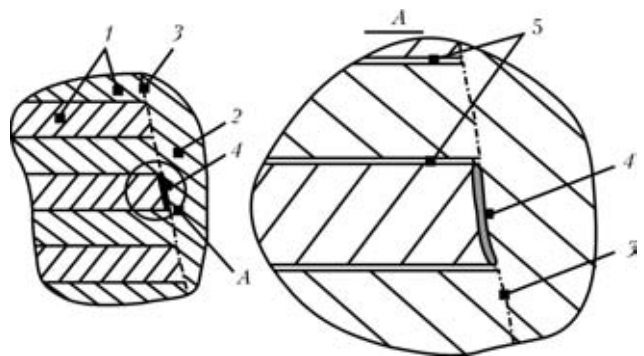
Зона відриву шару рулонної обичайки, утворена у зварному з'єднанні багатошарової посудини: 1 — шари рулонної обичайки; 2 — зона наплавленого металу; 3 — межа сплавлення основного і наплавленого металу; 4 — площинний дефект (зона відриву рулонної обичайки); 5 — зазори між шарами рулонної обичайки
